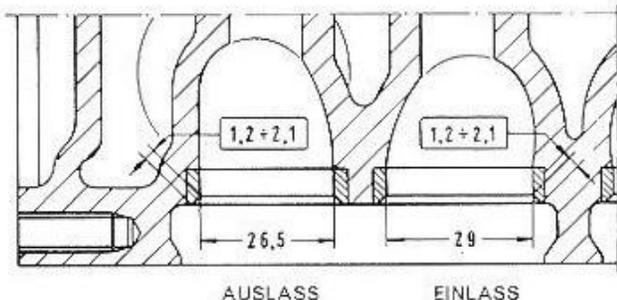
Die wichtigsten Angaben über die Ventilsitze im Zylinderkopf.
